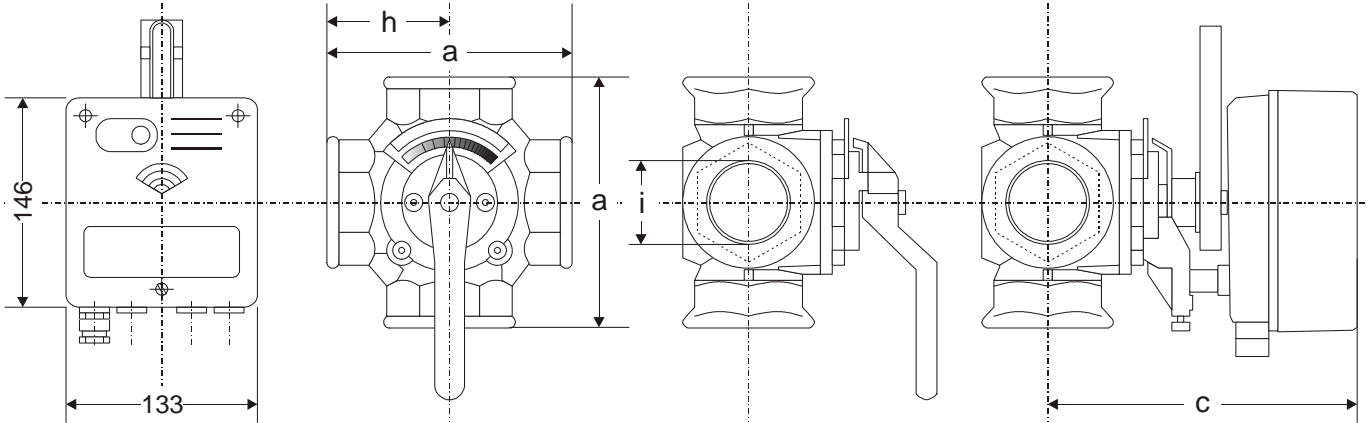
VMM et ZRxxxMA, dimensions (en mm)
